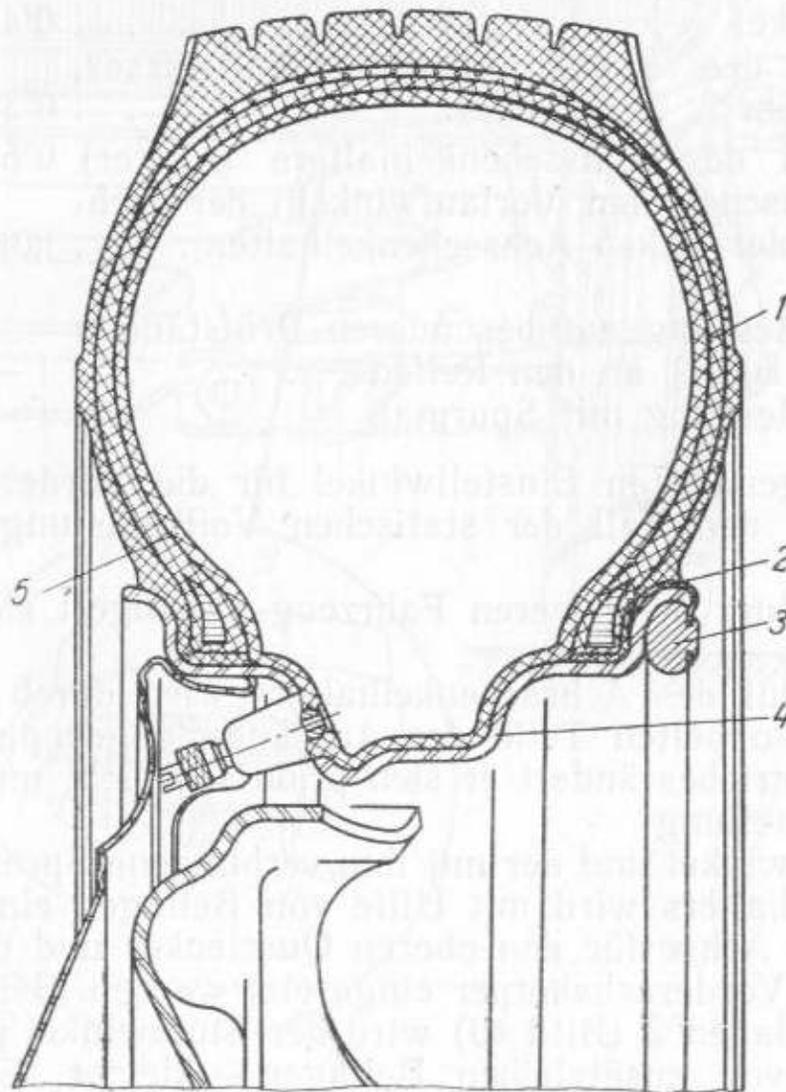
Befestigung des Auswuchtgewichtes an der Radfelge:
